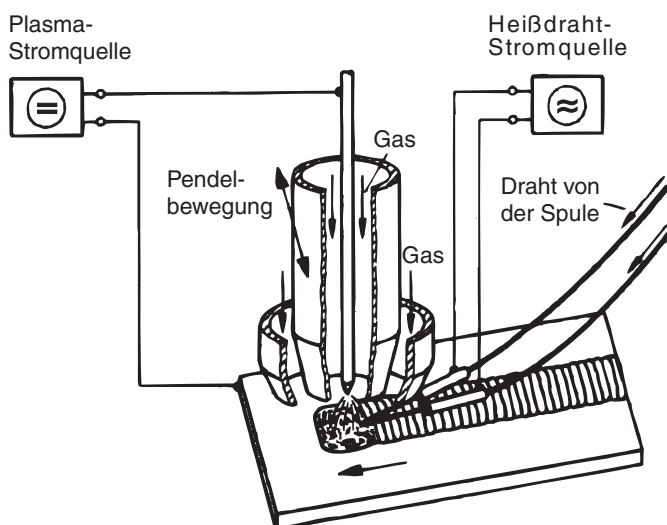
Prinzip des Plasmaheißdrahtschweißens
